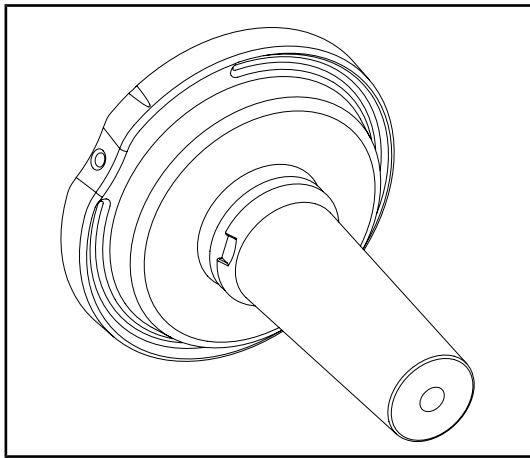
Держатель стерилизуемой рукоятки STG PSX
